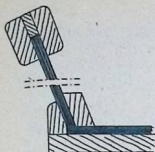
Ekan's enklare konstruktion framgår tydligt av detta tvärsnitt av bordläggningen.
